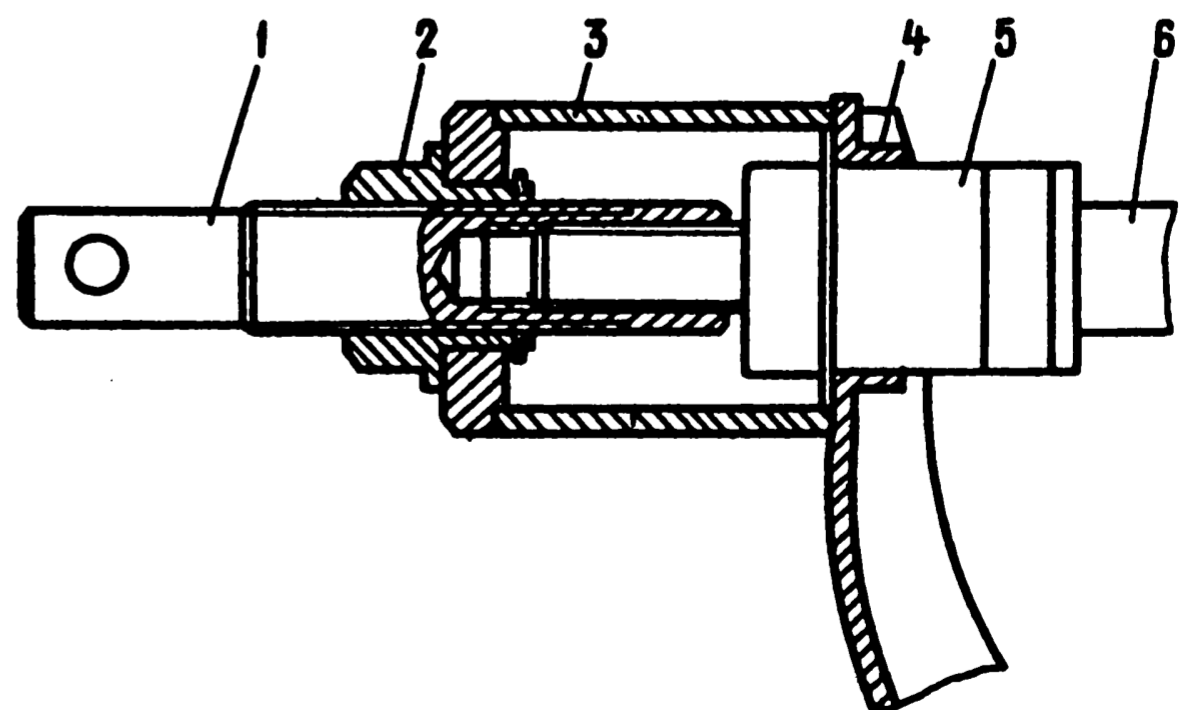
Схема выпрессовки шарнира нижнего рычага с помощью приспособления 02.7823.9500: 1 - винт; 2 - гайка; 3 - стакан; 4 - нижний рычаг; 5 - шарнир; 6 - ось нижнего рычага
